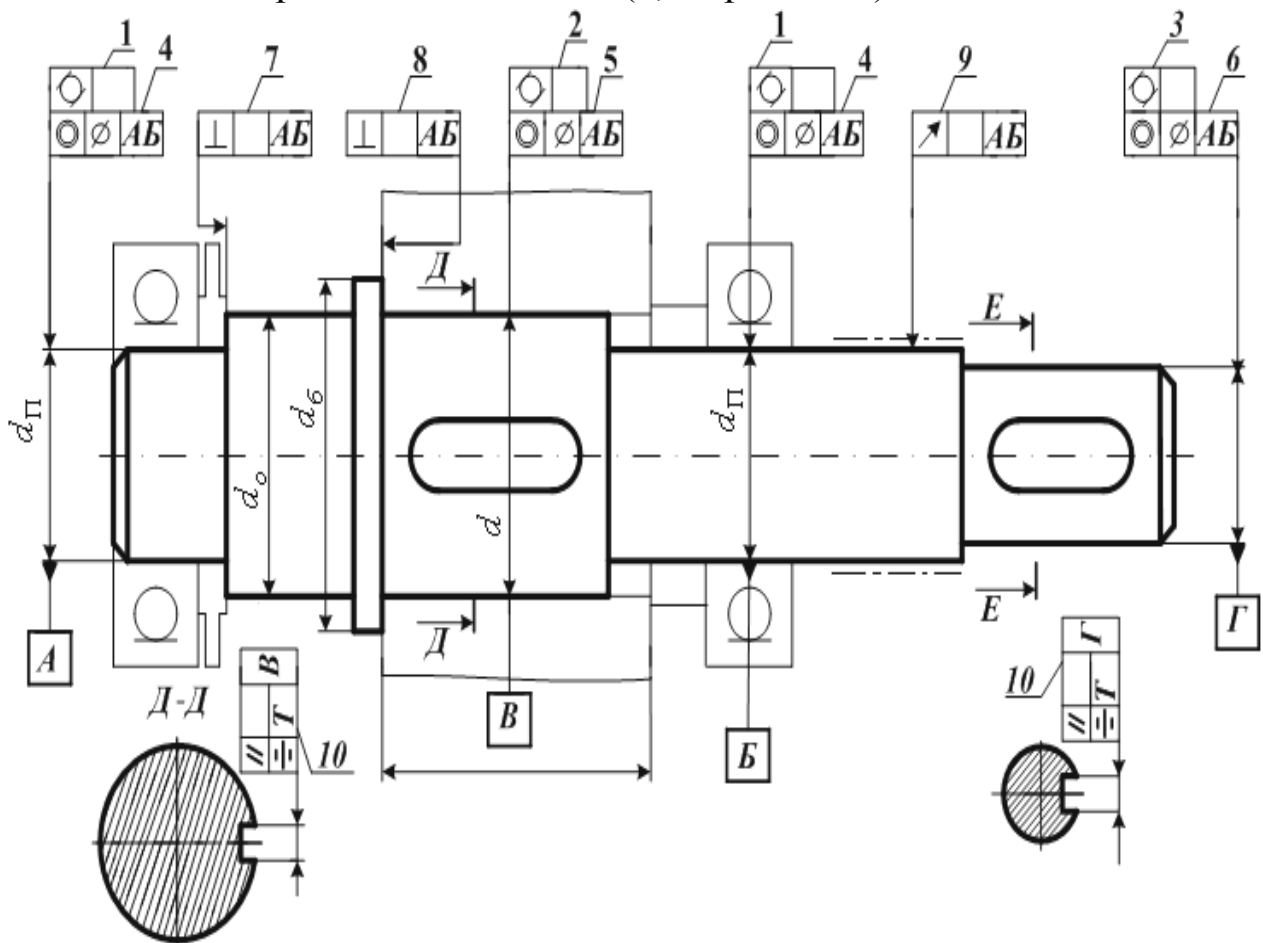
Позначення допусків форми і розташування поверхонь вала на креслениках
